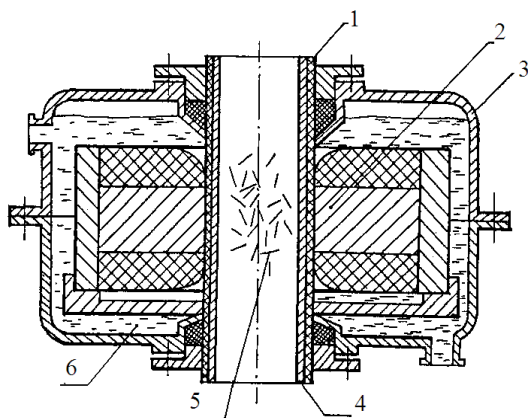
Принципова схема апарату з вихровим шаром: 1 — корпус з немагнітного матеріалу; 2 — індуктор ОЕМП; 3 — металева сорочка; 4 — робоча камера апарату; 5 — феромагнітні частинки; 6 — трансформаторне масло для охолодження
